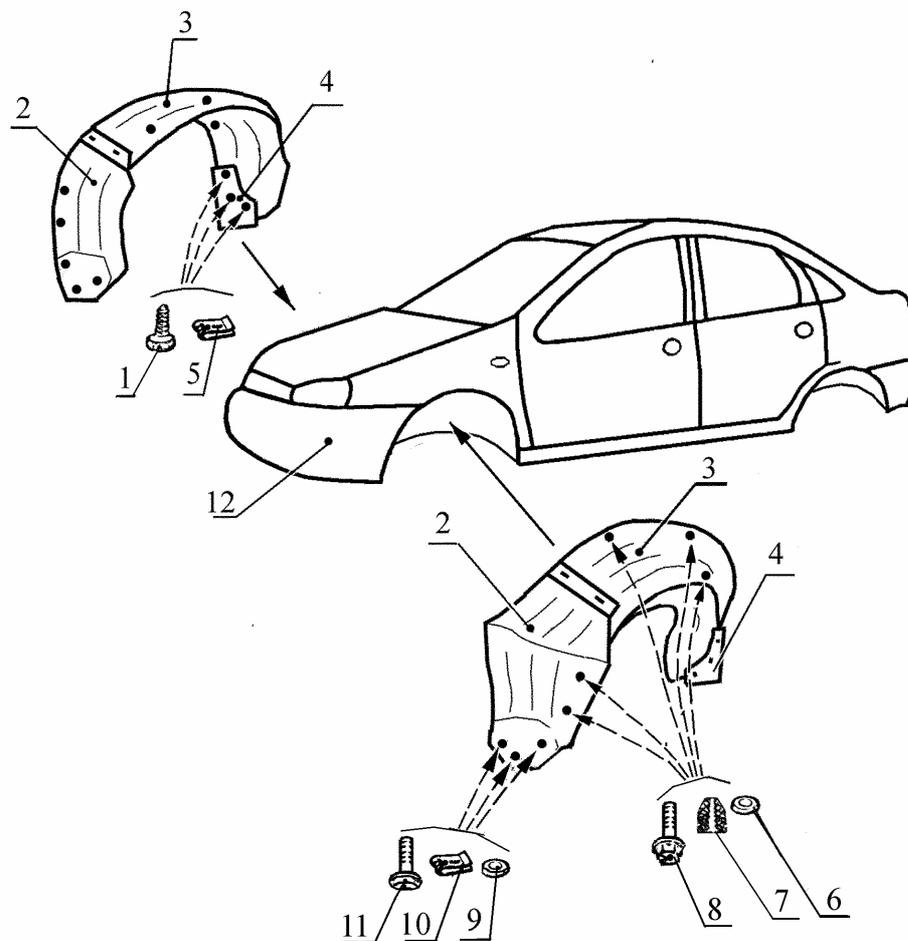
Щиток, защитный кожух и фартук переднего крыла:
